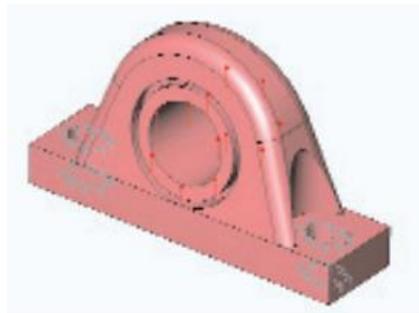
Aplicación de cargas a la pieza (Fuente: citado por [20]).
